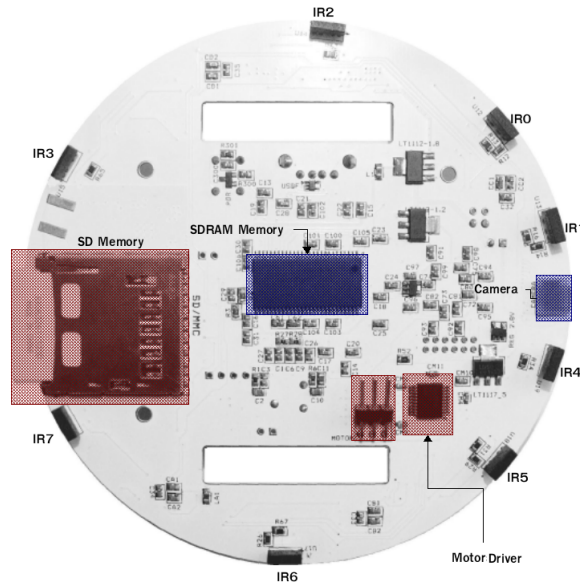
Lado de soldadura de la tarjeta principal de ECBOT.
